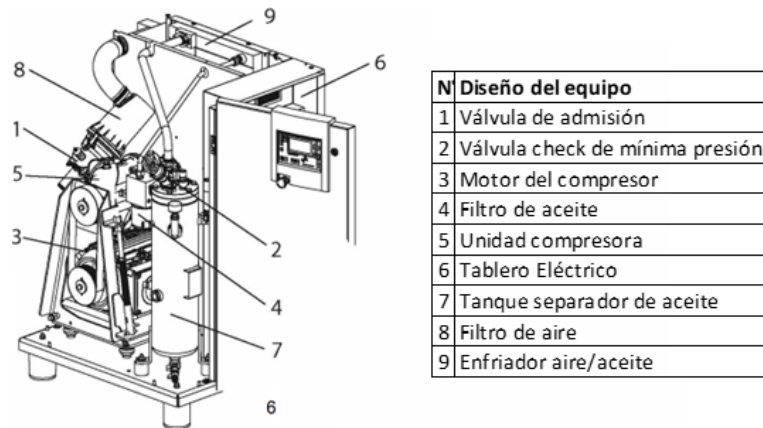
Partes de unidad compresora tipo C27 Kaeser
